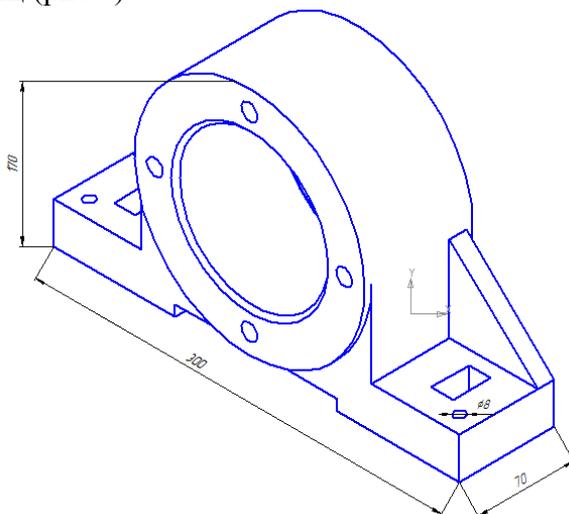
Аксонометрический чертёж детали «Корпус».
